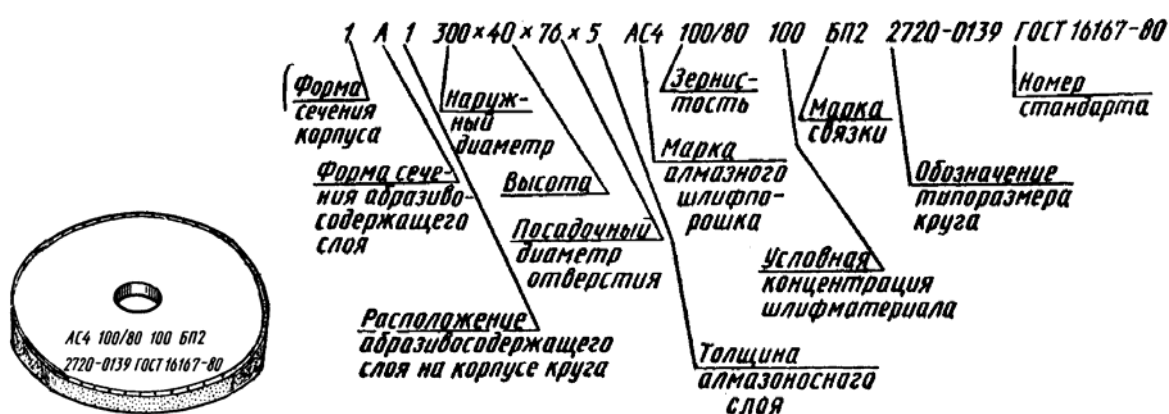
Маркировка и условное обозначение алмазного инструмента
